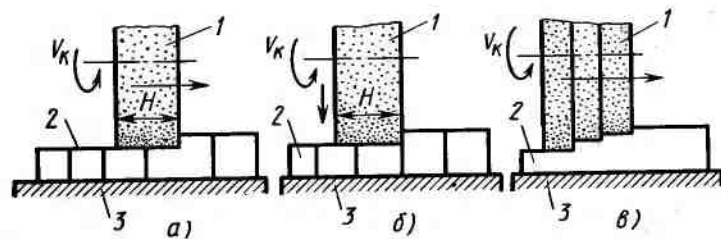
Схемы шлифования периферией круга на станках с прямоугольным столом:
